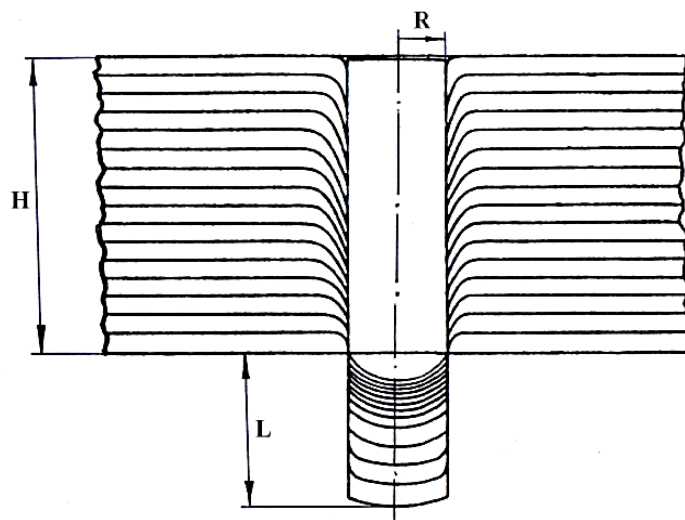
Схема деформации многослойной свинцовой заготовки при прошивке
